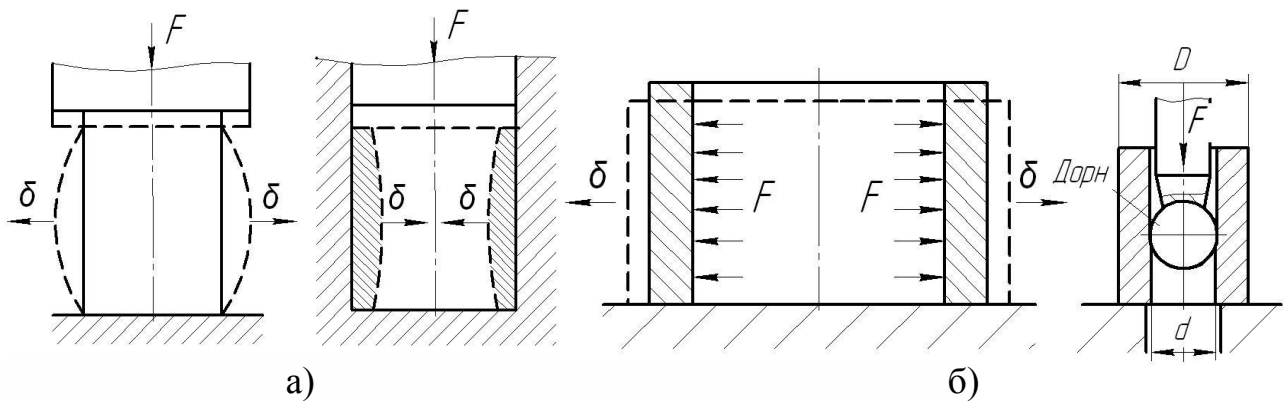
Схема осадки а) і роздачі б) деталей
